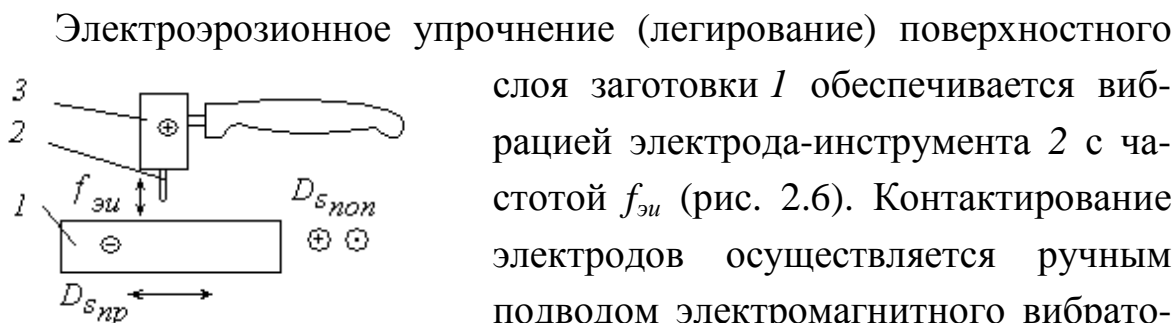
Схема электроэрозионного упрочнения поверхности заготовки
